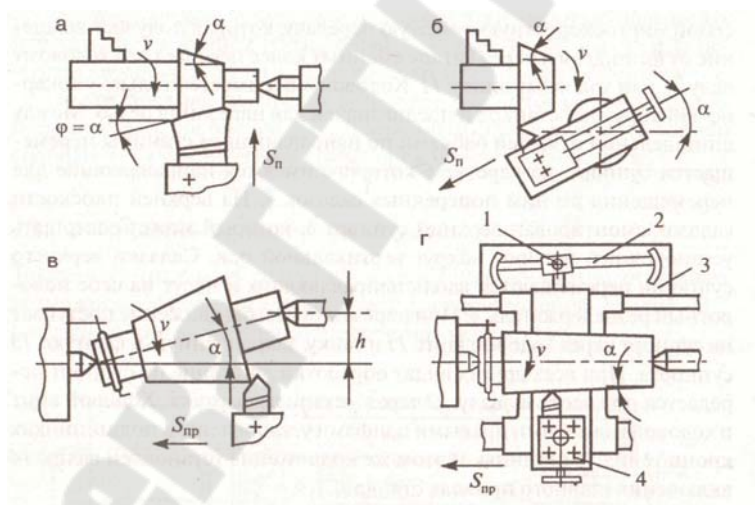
Схемы обработки конических поверхностей на токарно-винторезном станке
